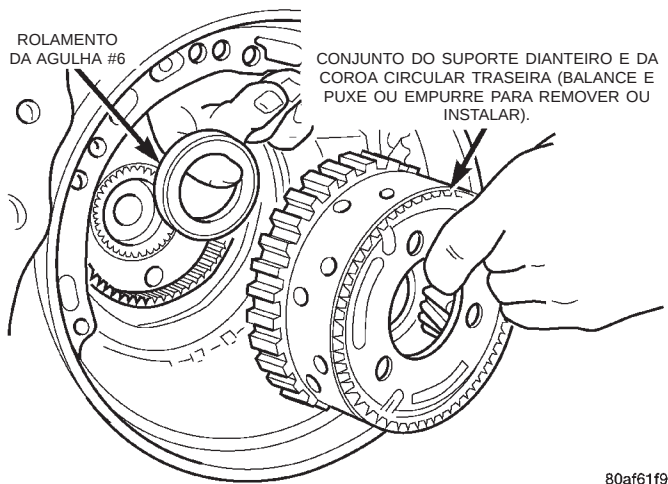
Instalação do Conjunto do Suporte Dianteiro e da Coroa Circular Traseira
